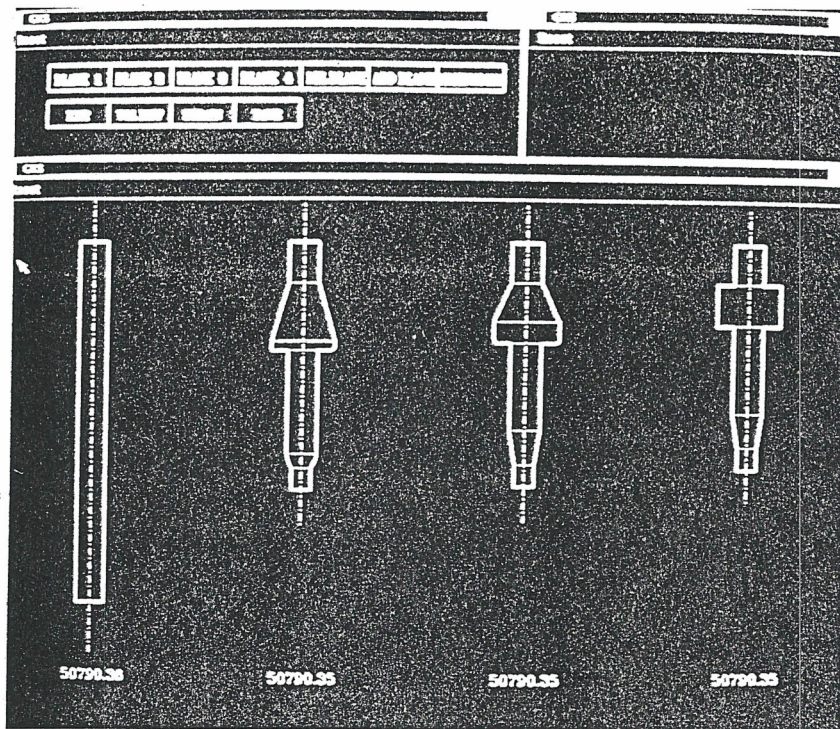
Sequenza di stampaggio per il componente di Fig. 5
